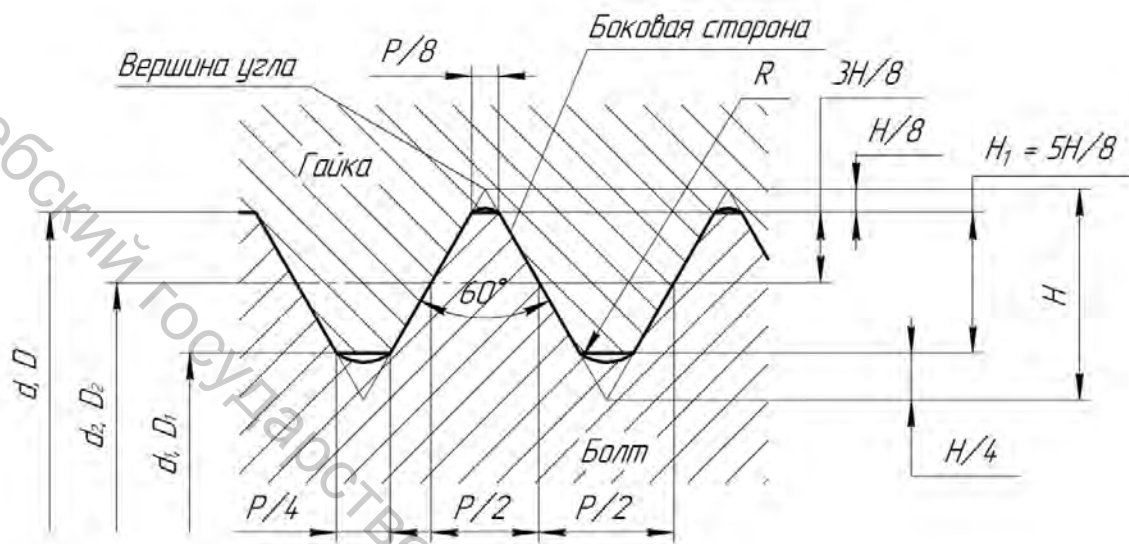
Профиль метрической цилиндрической резьбы
